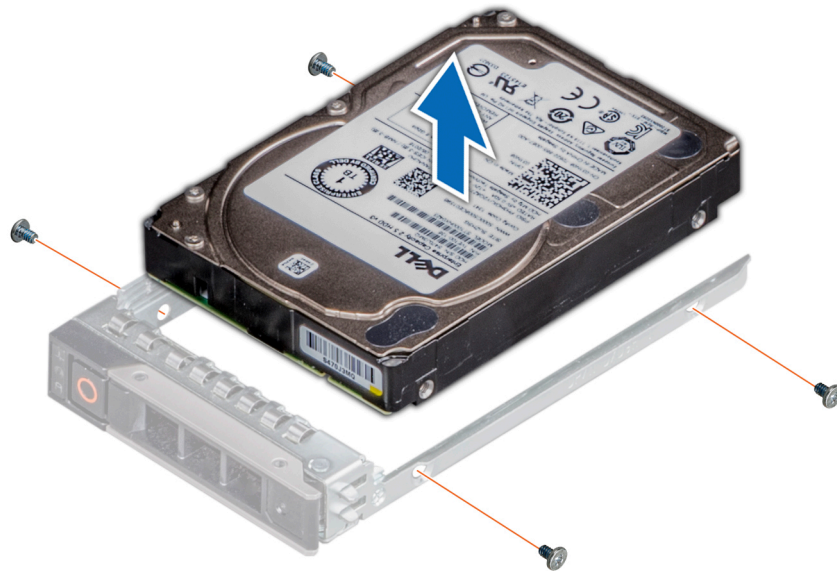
Laufwerk aus Laufwerksträger entfernen
